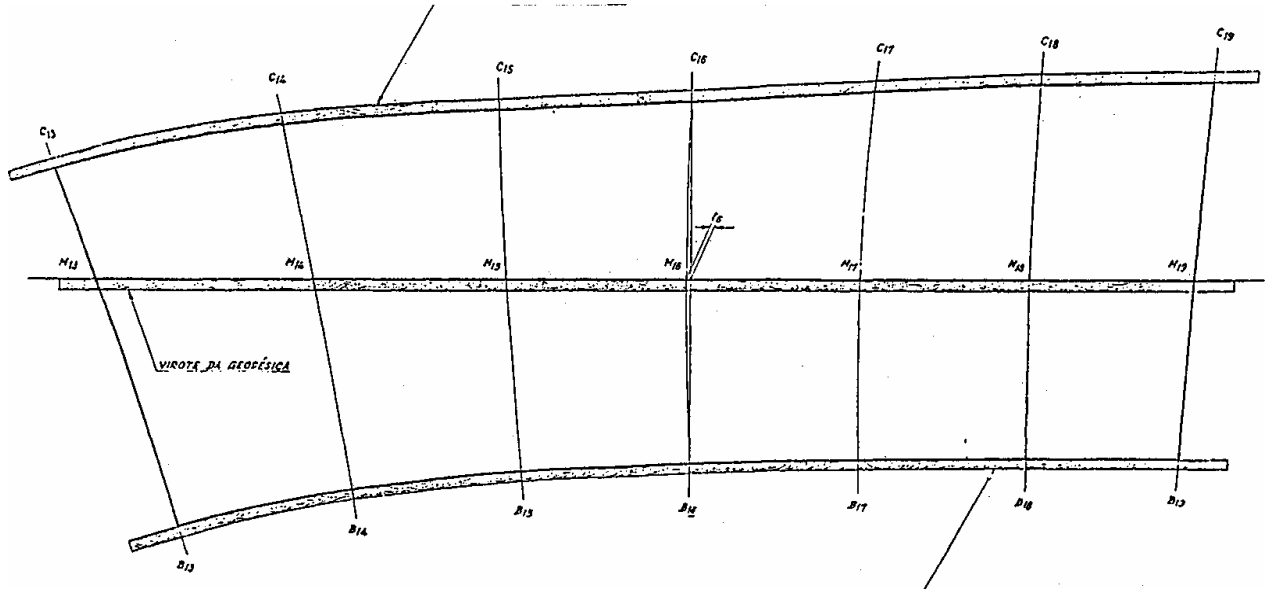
PLANIFICAÇÃO DA CHAPA
